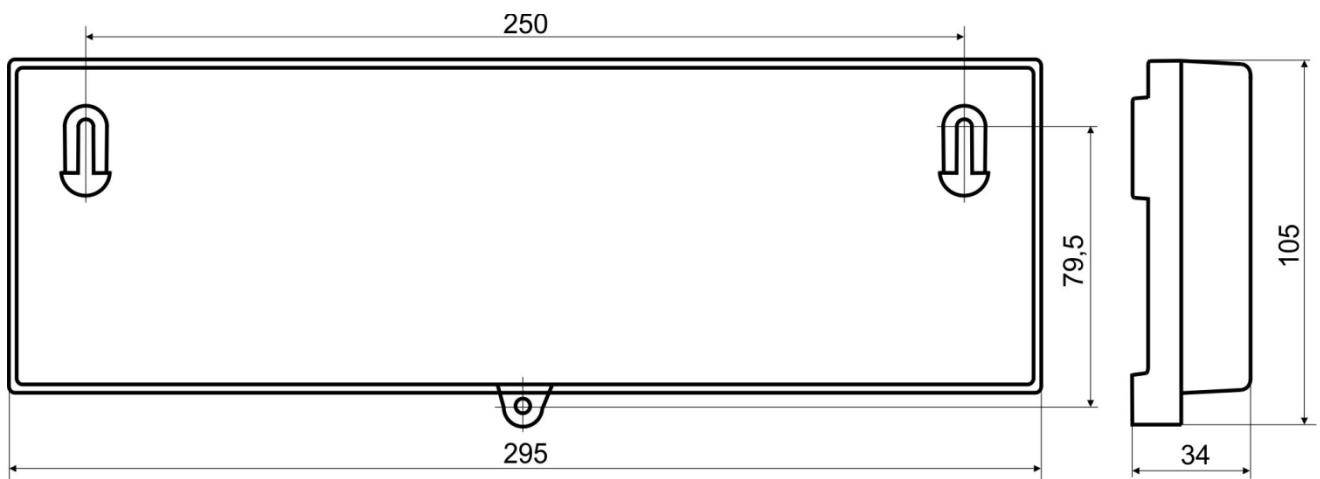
Габаритные и установочные размеры блока клавиатуры
